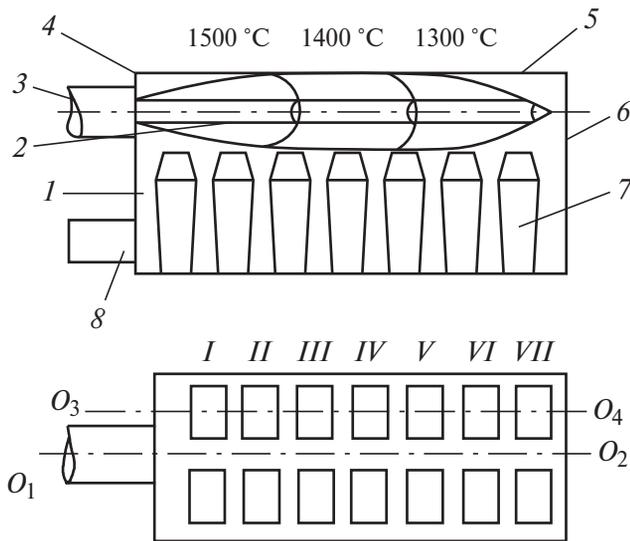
Схема рекуперативного нагревательного колодца с верхней горелкой:
